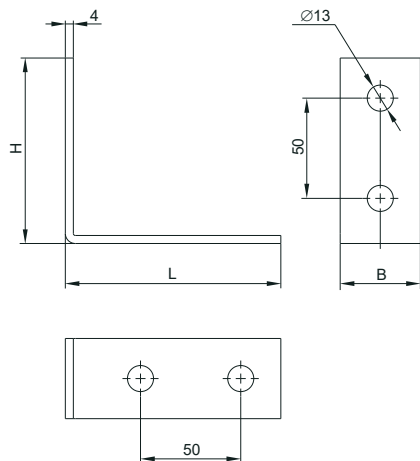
Уголок крепежный двойной для STRUT-профиля / Figure F.2 – Double fastening angle for STRUT profile
